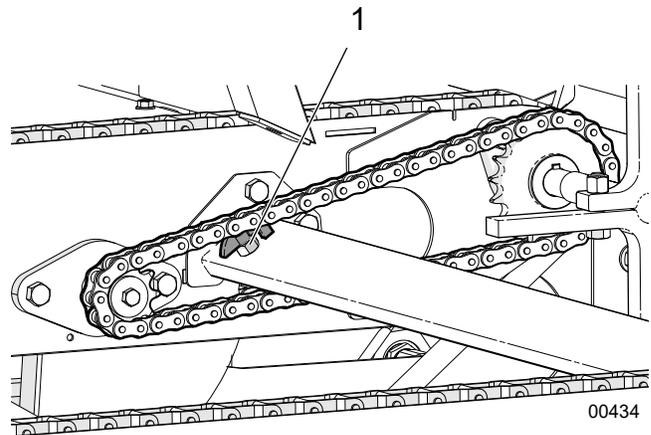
Chaîne d'entraînement du plateau de chargement avec convoyeur
